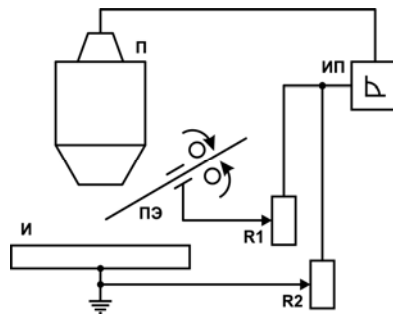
Схема плазменной наплавки с токоведущей присадочной проволокой:
